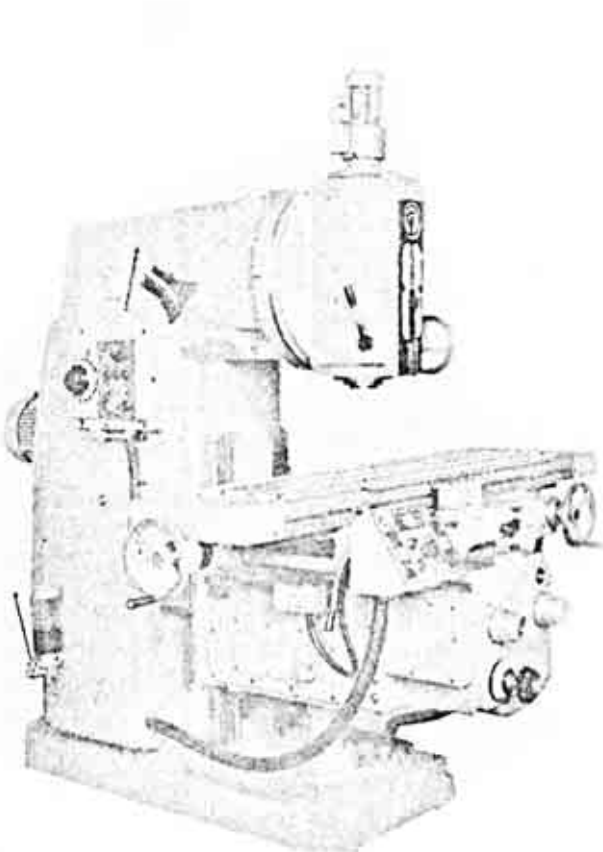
Вертикальный консольно-фрезерный станок 6Т12
